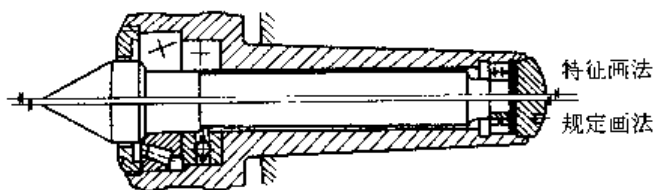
圆锥滚子轴承、推力球轴承和双列深沟球轴承在装配图中的画法
